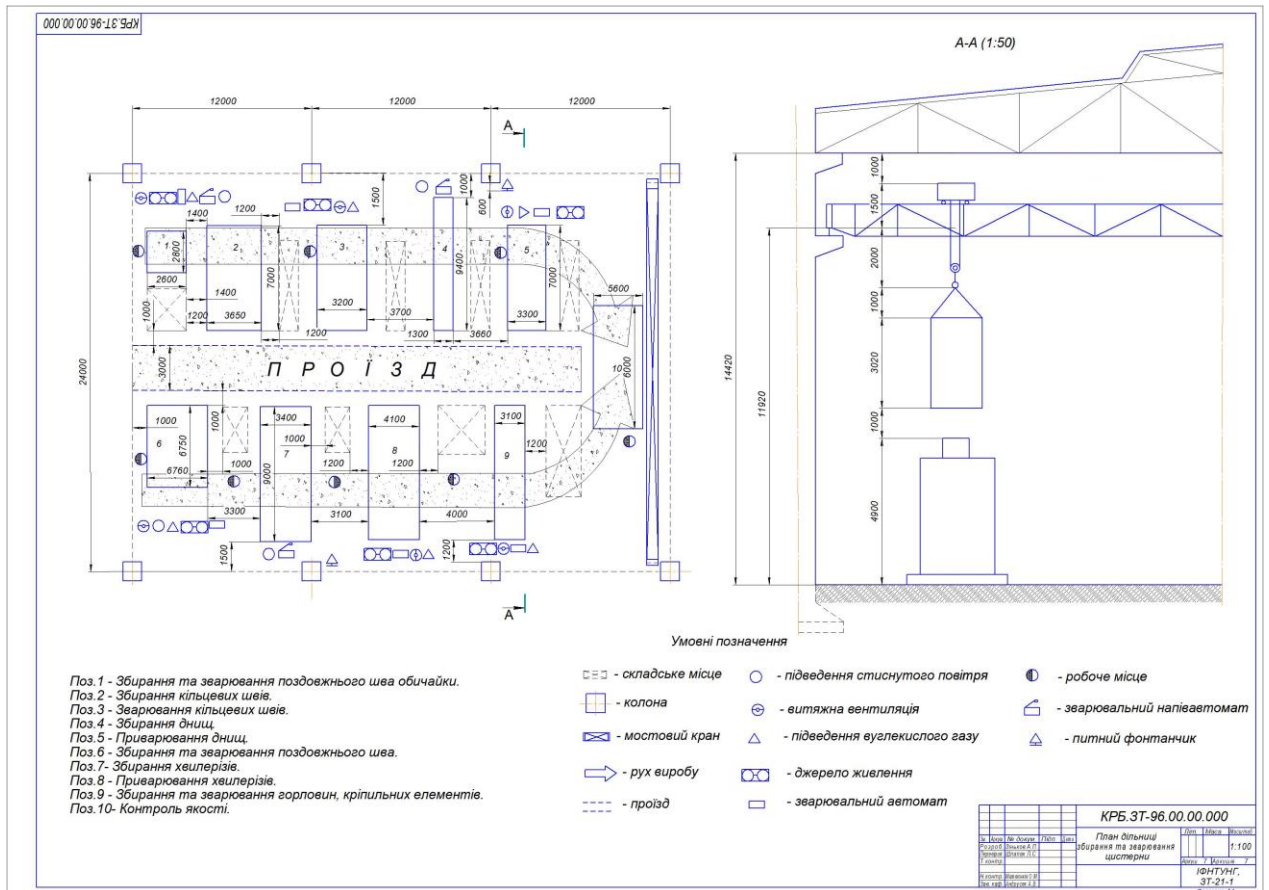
План дільниці для виготовлення корпусу резервуару
